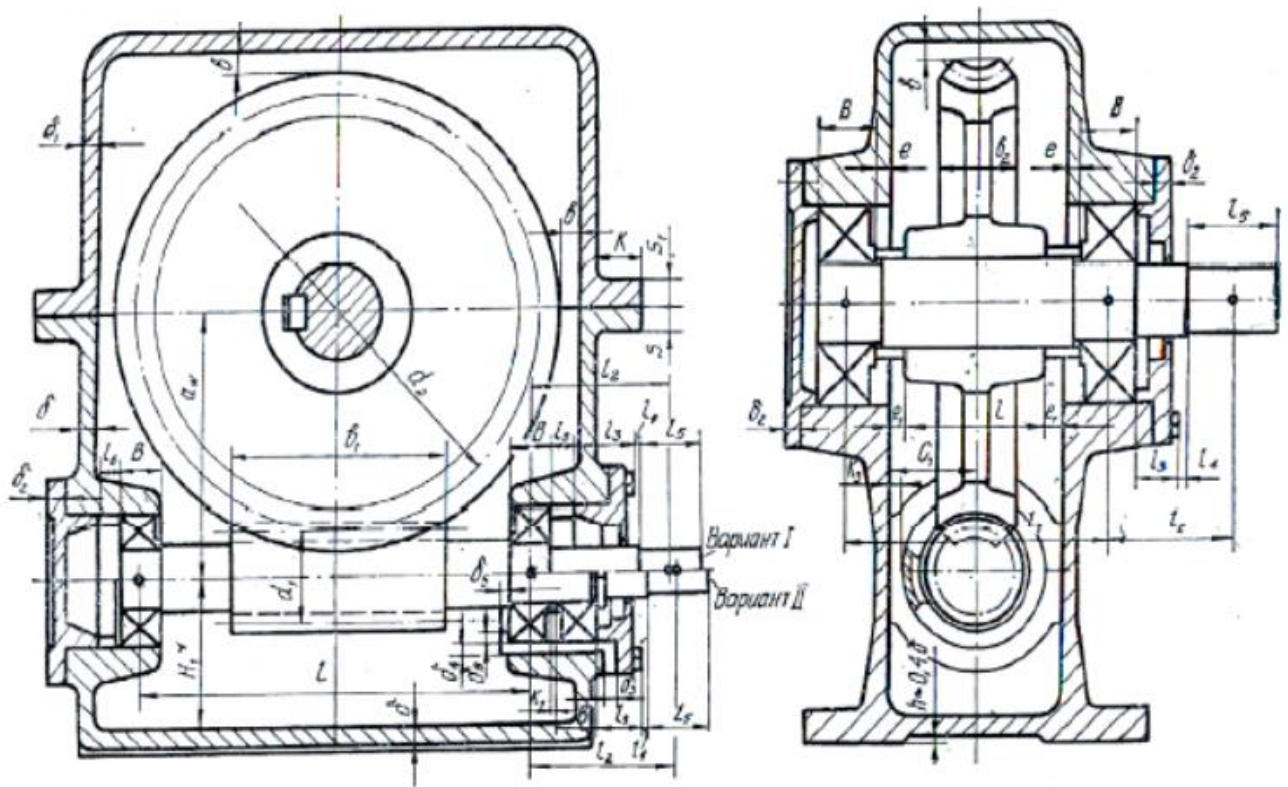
Ескізна компоновка одноступінчастого черв'ячного редуктора
